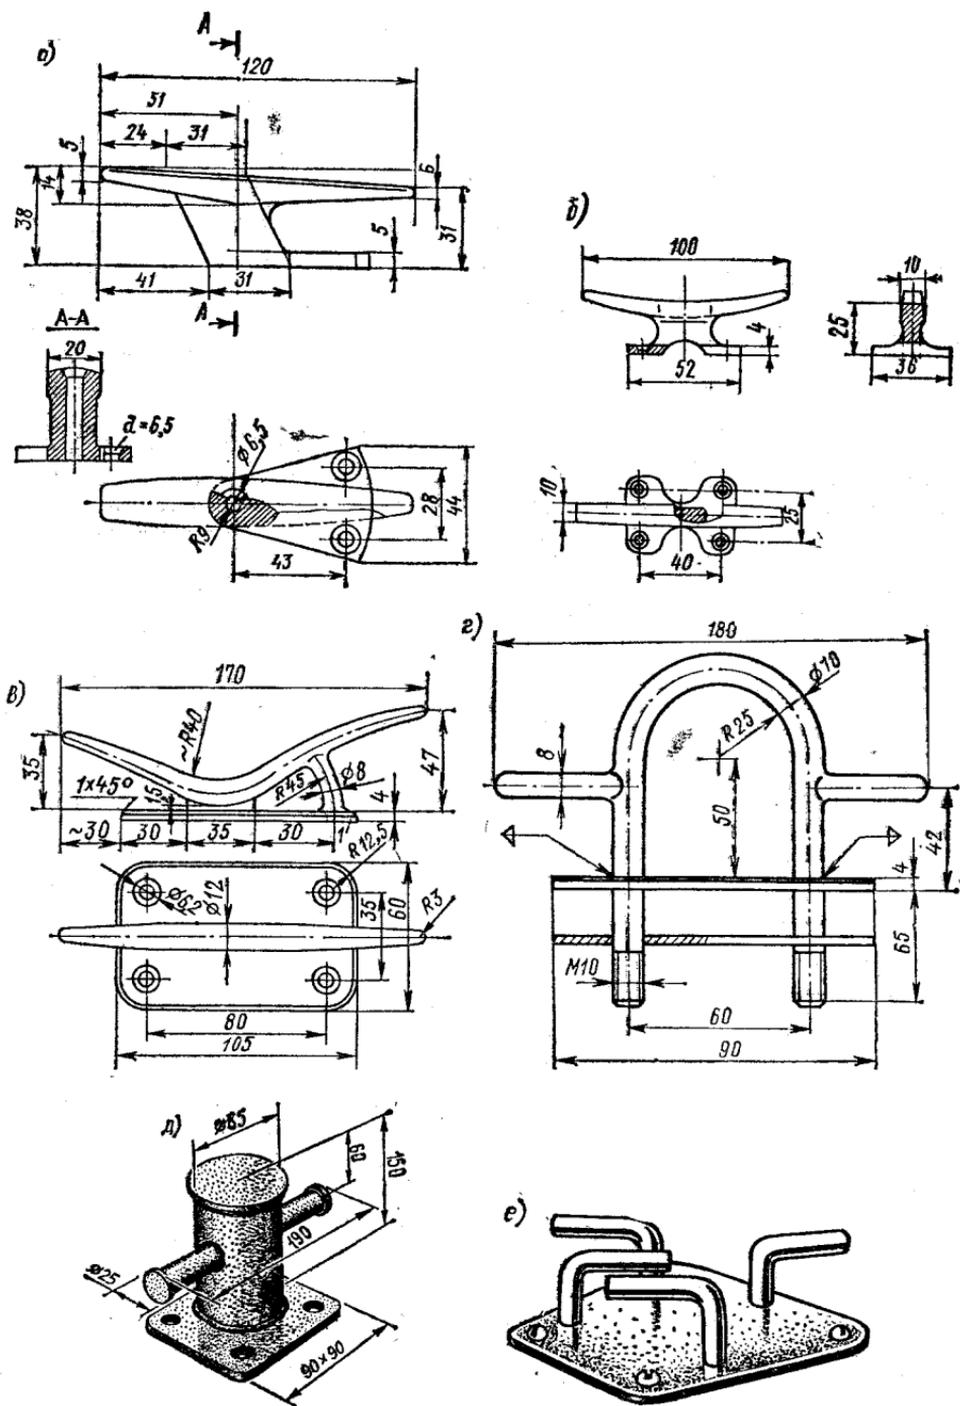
Детали якорно-швартового устройства: а, б, в — утки; г — рым, совмещенный с уткой; д — крестовый шнехт; е — утка, совмещенная с киповой планкой.
